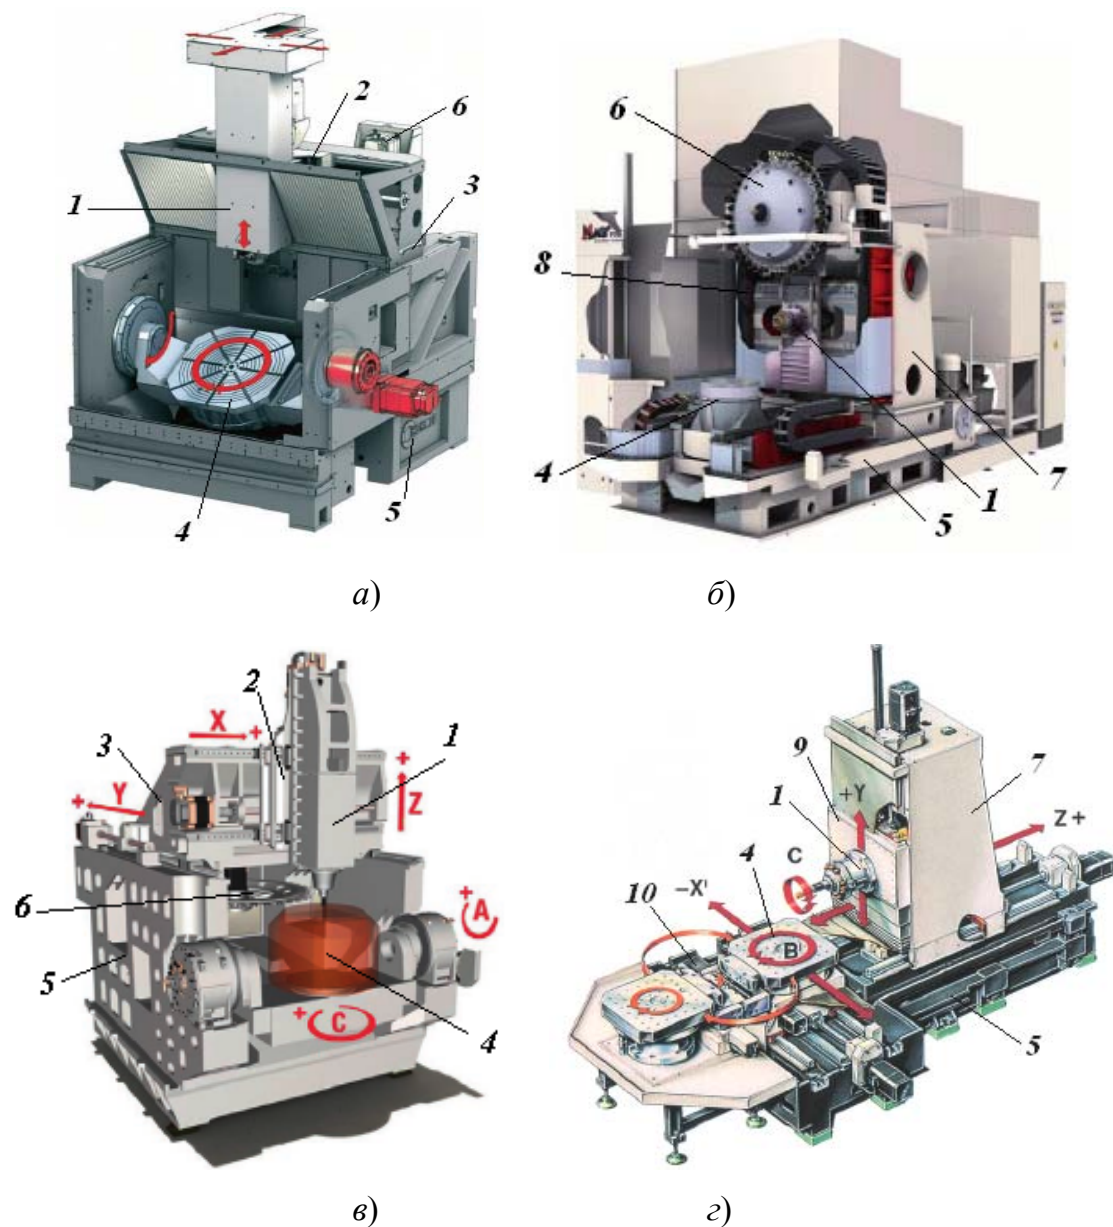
Компоновки комплексных станков с ЧПУ:
